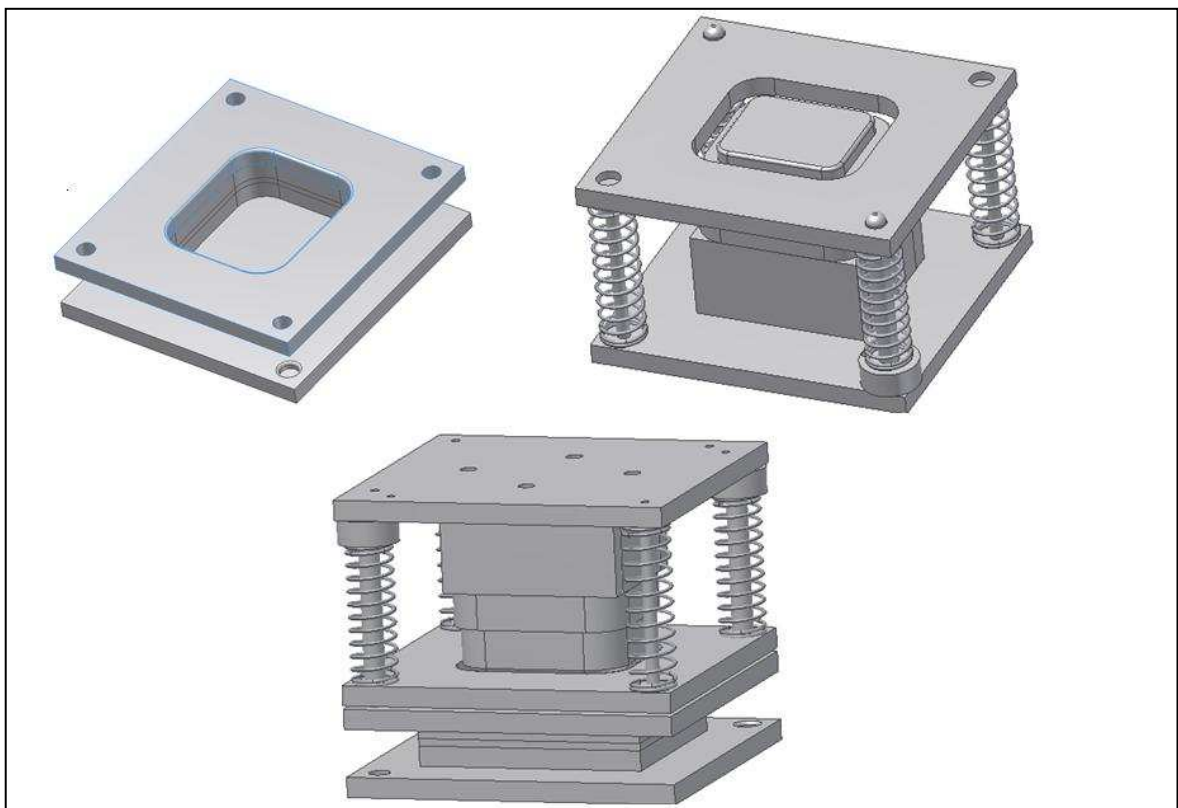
Molde macho-hembra final construido en acero ASTM A-36.
